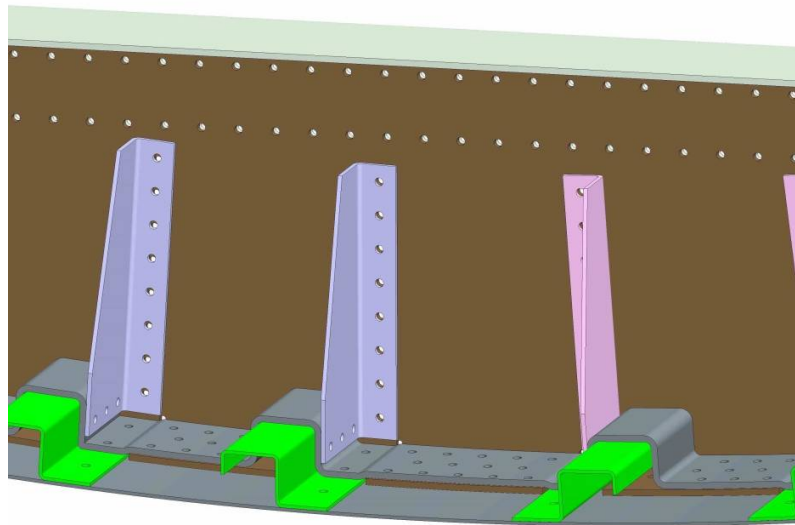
Dettaglio del collegamento tra la parete posteriore (marrone) ed il fondo. Da notare l'elemento di rinforzo sagomato (grigio) che passa sopra ai correntini ed alla parte piegata della lamiera della parete posteriore.
